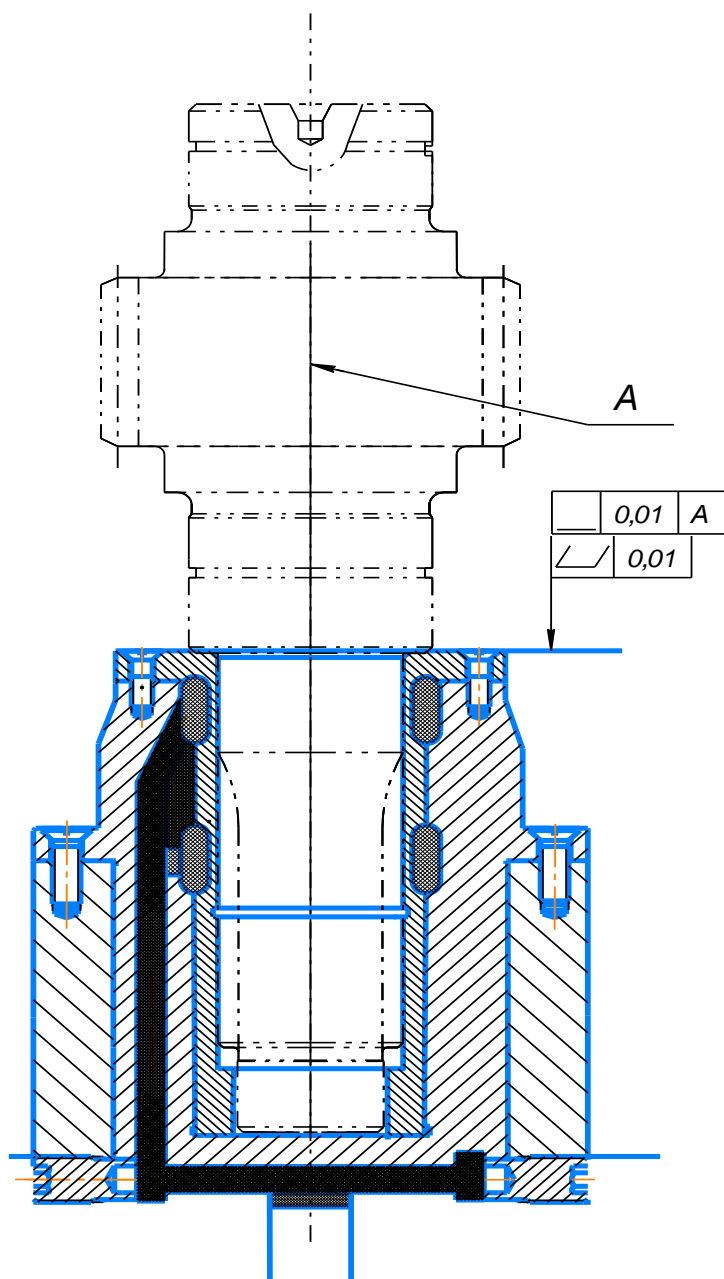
Принципиальная схема приспособления при обработке на зубофрезерном станке с ЧПУ NGH-180
